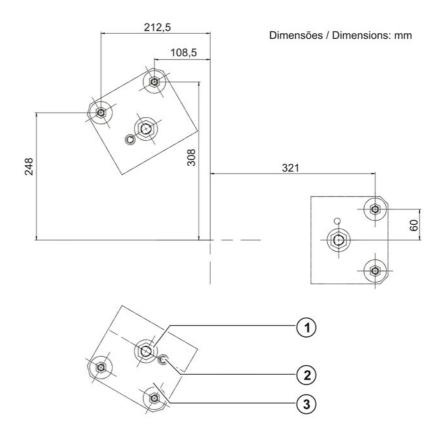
Fixação em fundação com centragem, desenho dimensional
